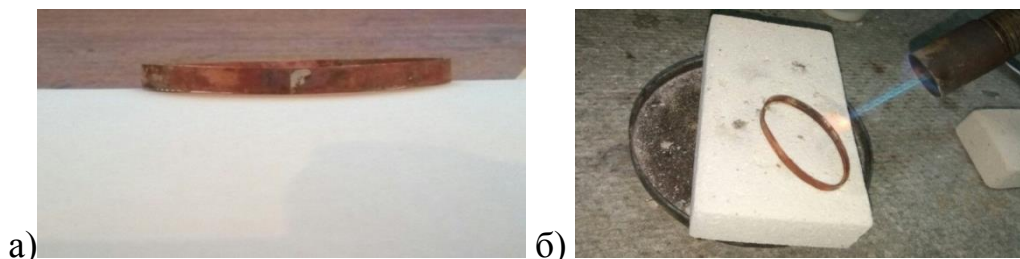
Припой серебряный а) Заготовка для каста, б) Пайка каста
